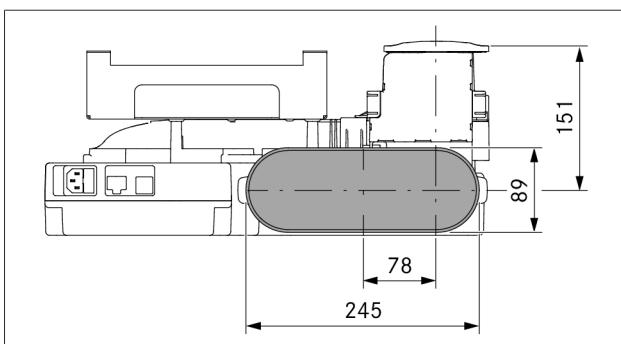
Rozmery pripojenia potrubia PKA3/PKA3AB s kolenovou potrubnou priechodkou
